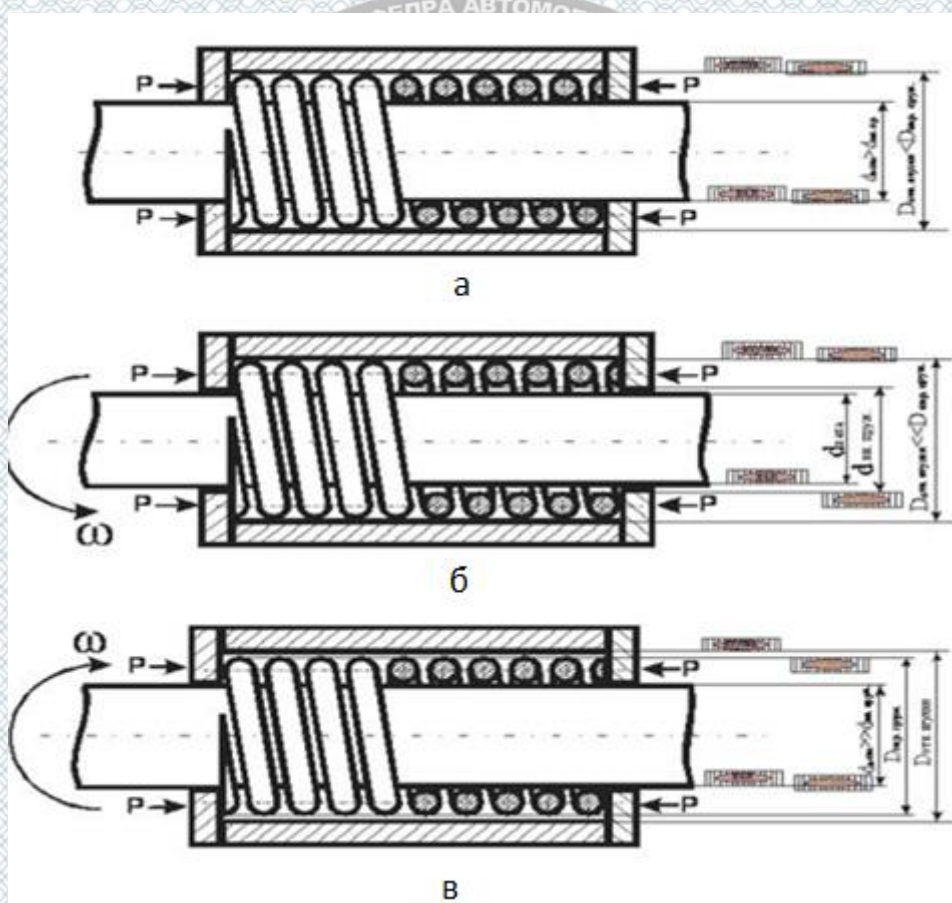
Схема посадок на робочих поверхнях шарнірного підшипника з пружним пружинним вкладишем: а - підшипник знаходиться в спокої; б і в - обертання осі (цапфи) в різні боки
